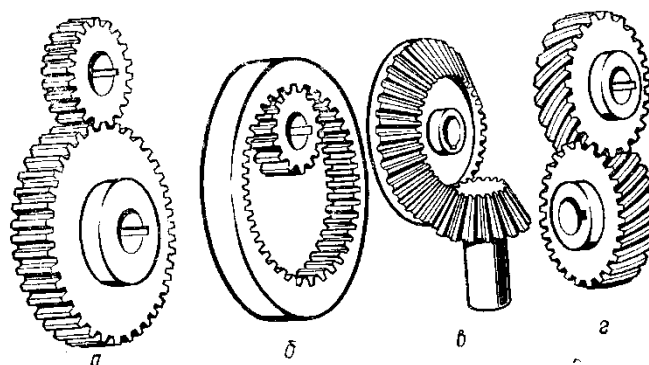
Зубчатые передачи: а – цилиндрическая прямозубая с наружным зацеплением; б – цилиндрическая прямозубая с внутренним зацеплением; в – коническая прямозубая; г – цилиндрическая винтовая.
